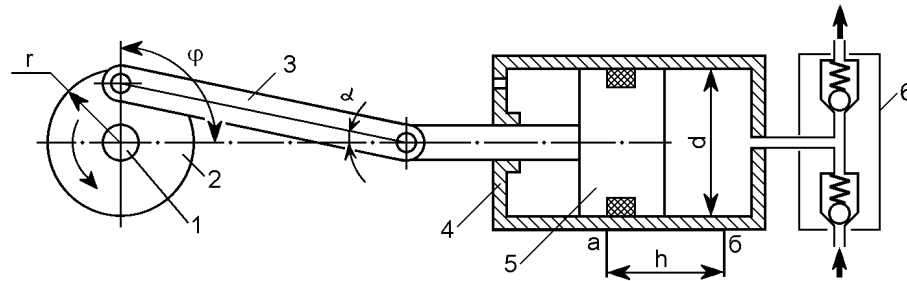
Схема поршневого насоса с кривошипно-шатунным приводом: 1-вал; 2-кривошип; 3-шатун; 4-цилиндр; 5-поршень; 6-клапанная коробка
